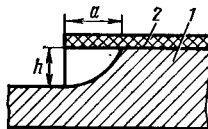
Схема бокового подтравливания при размерном травлении: 1 — заготовка; 2 — пленка защитного покрытия
